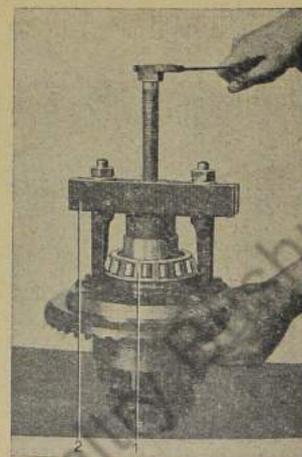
Kegelrollenlager vom Ausgleichgehäuse abziehen
